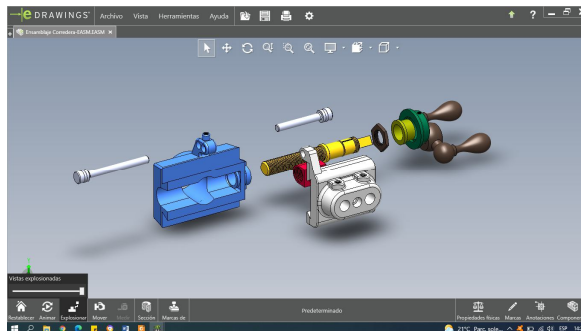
Conjunto mecánico explotado mostrando la disposición de las piezas.
